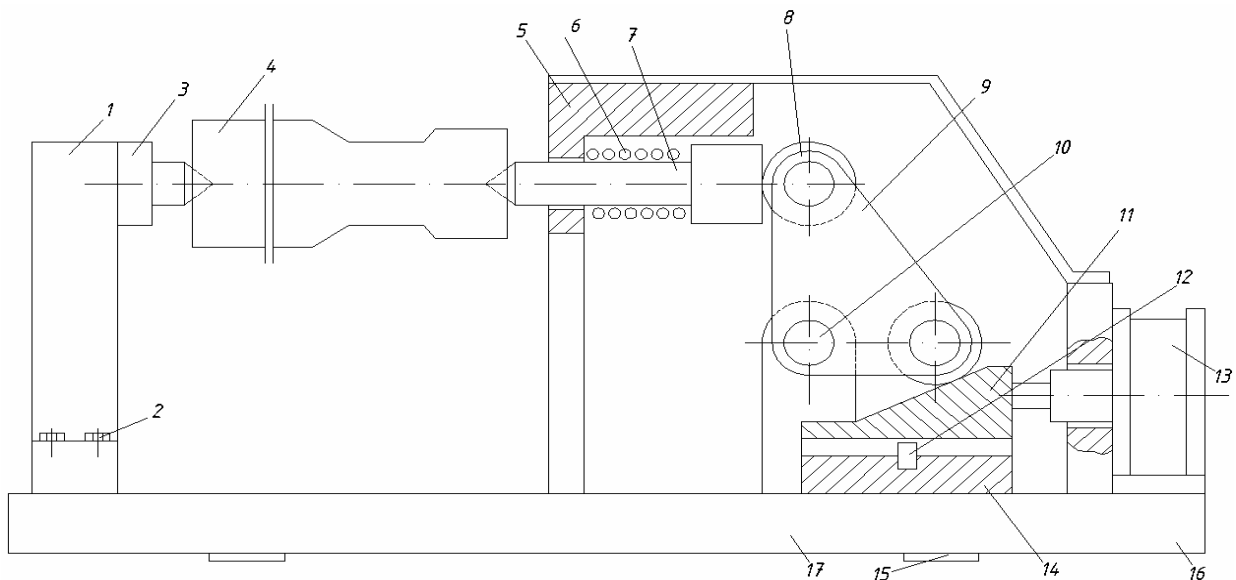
Приспособлення для фрезерування двох пазів
